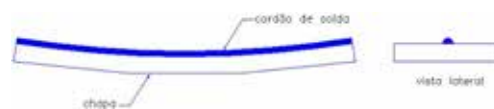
Distorção ocasionada pelo cordão de solda.
